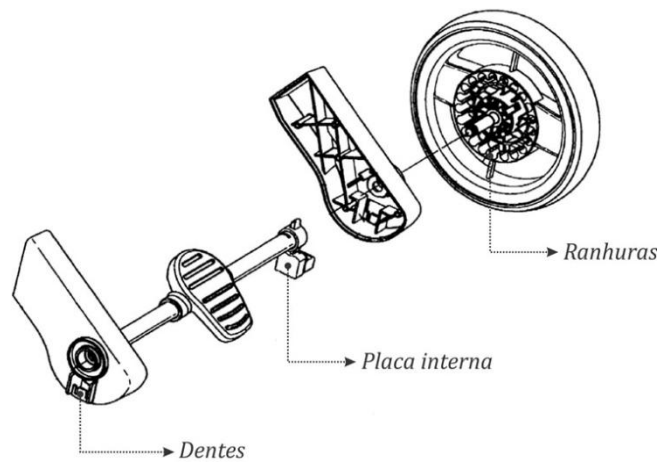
Vista explodida do sistema de frenagem com seus componentes
